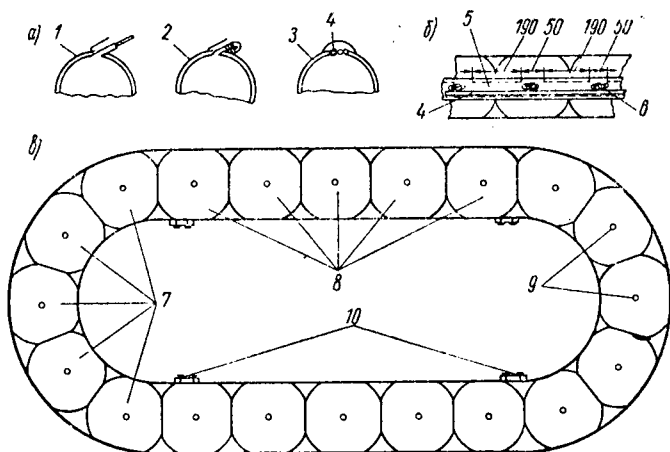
Надувная лодка: а — камеры; б — нашивка полоски под верхний каркас; в — схема расположения камер.
